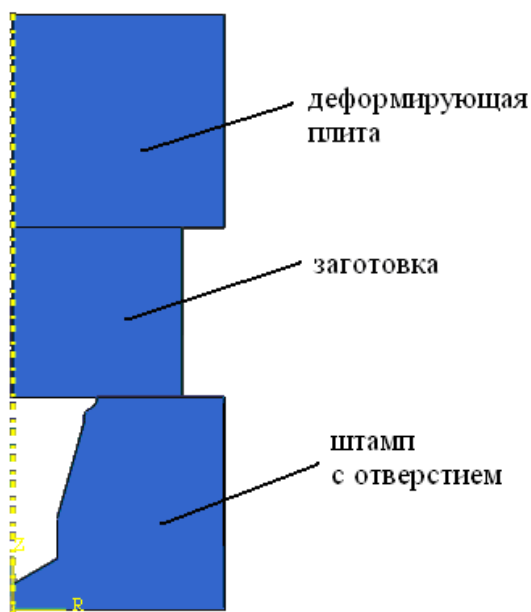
Сборка инструмента и заготовки в комплексе *Abaqus
